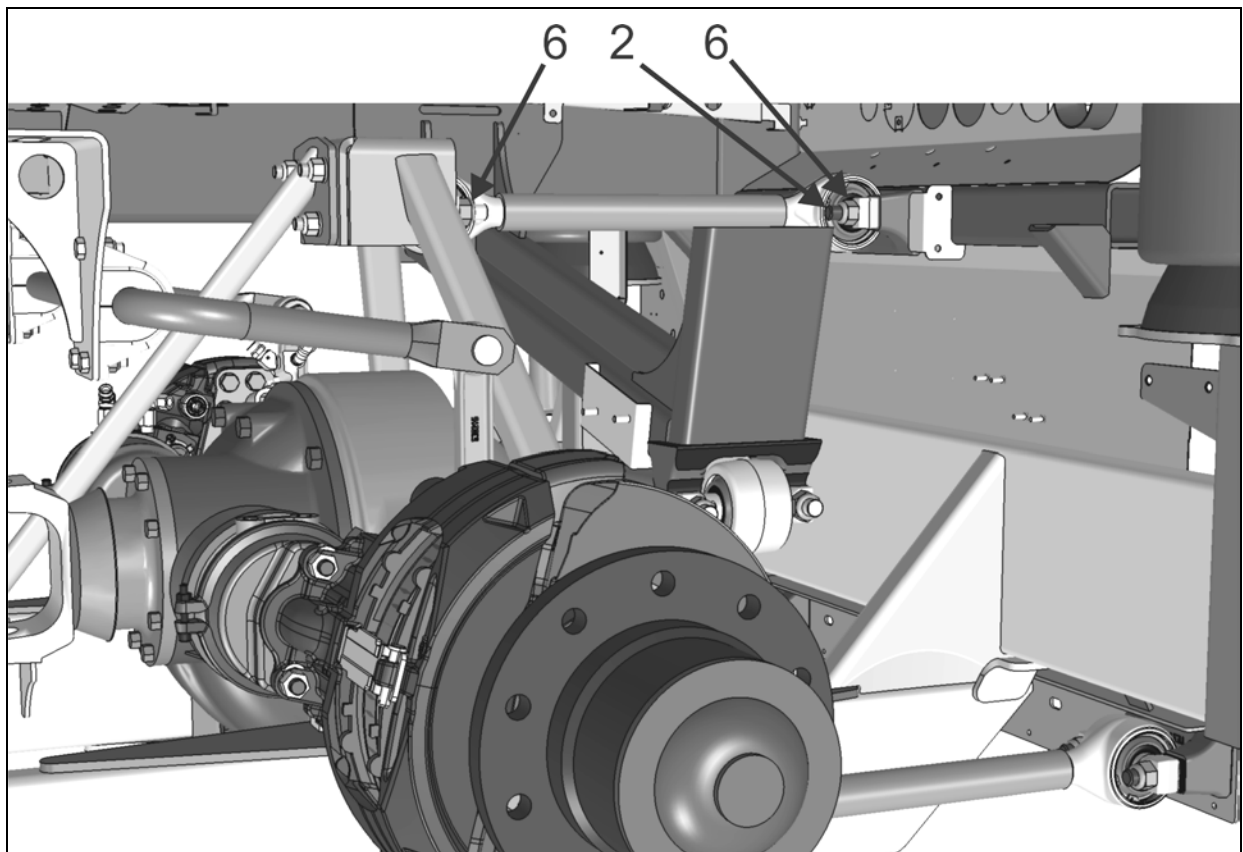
COUPLES DE SERRAGE – ESSIEU MOTEUR, HAUT
